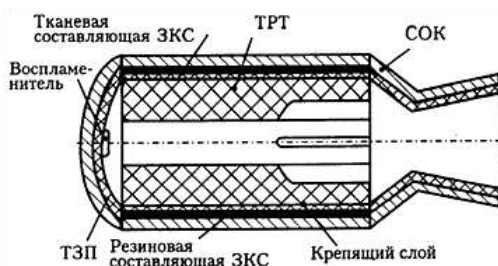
Схема крепления заряда с корпусом с помощью защитно-крепящих слоев
